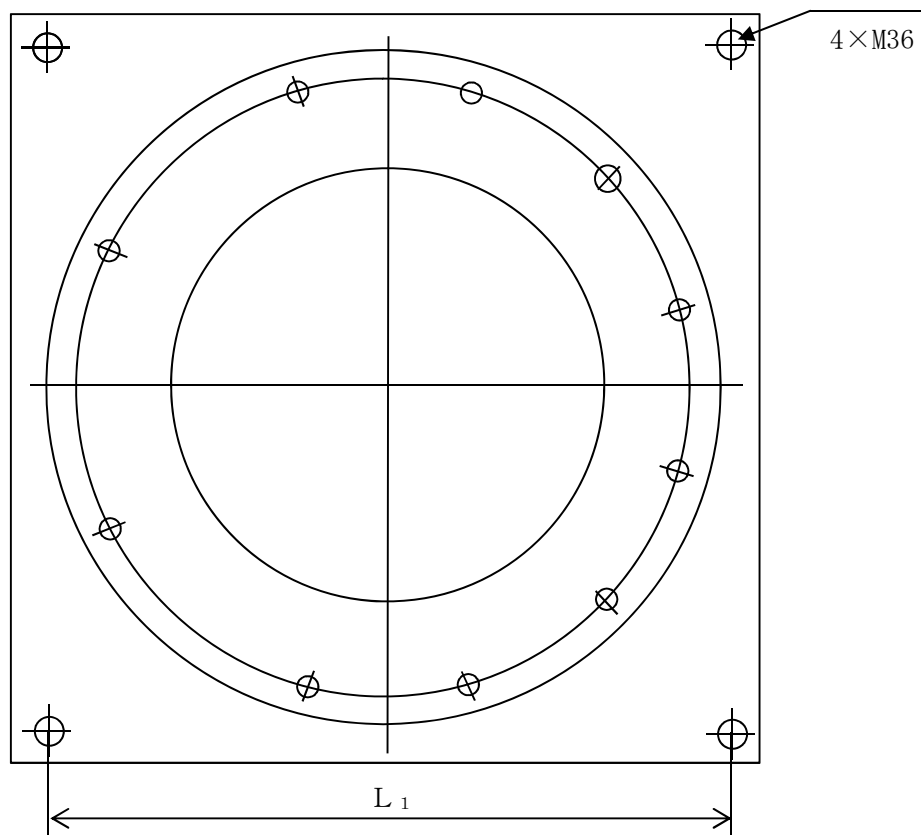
据付面基礎ボルトの各ボルト間寸法の配置図
